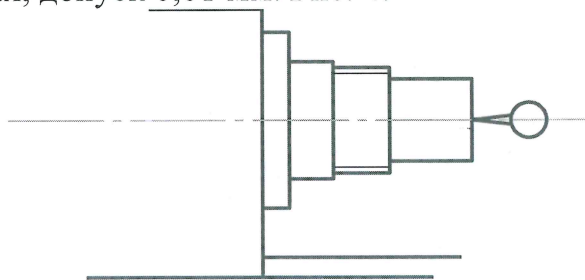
Схема установки индикатора для проверки осевого биения шпинделя
